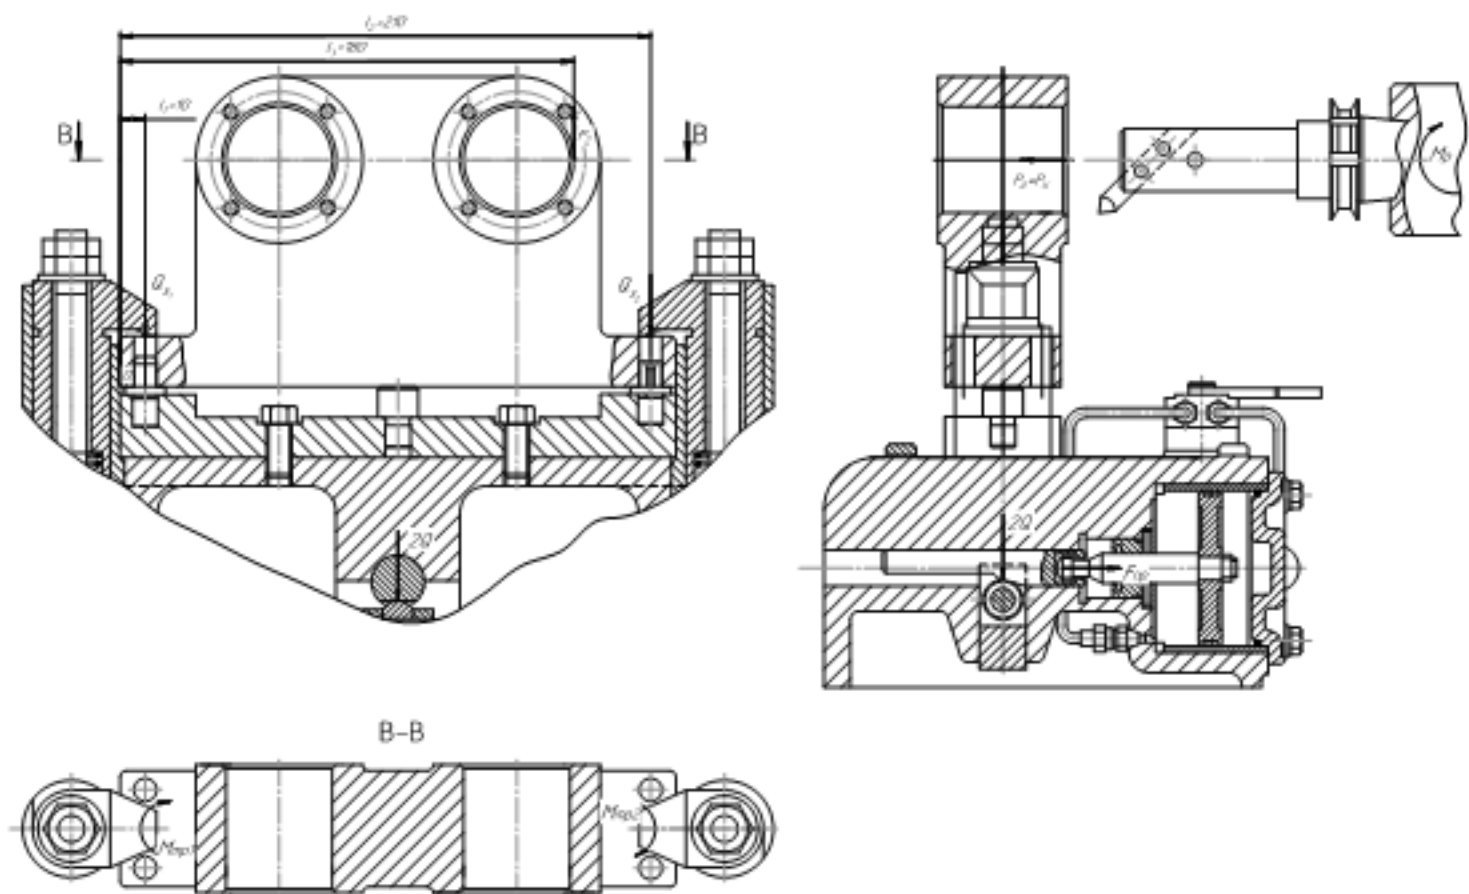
Схема сил, що діють на заготовку при розточуванні
